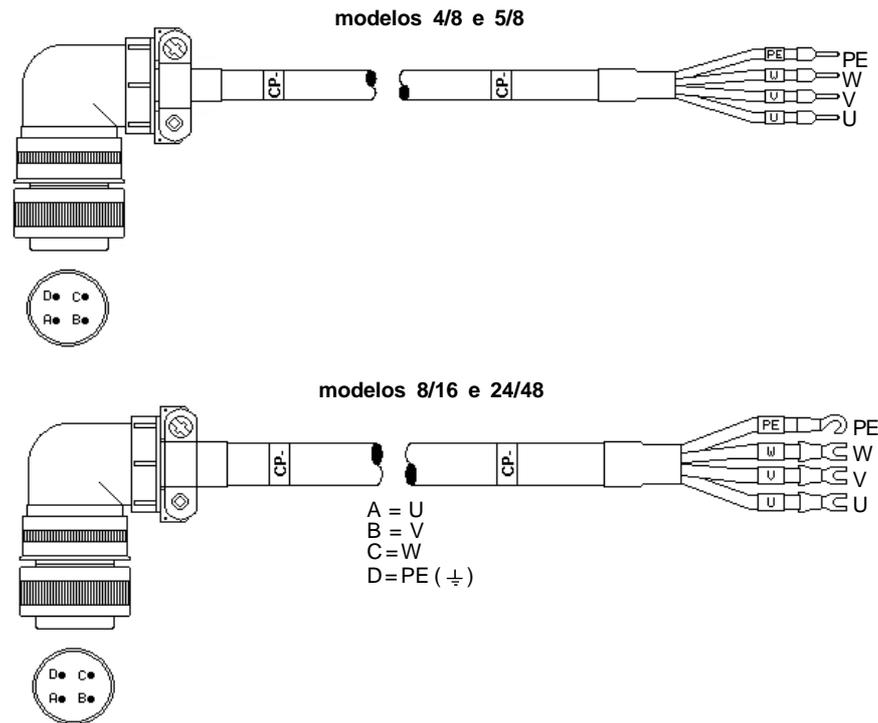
Desenho e pinagem do cabo de potência com conector 90°
